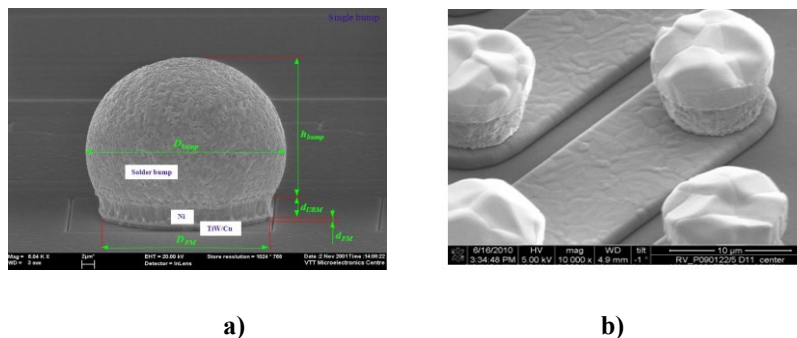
Exemples de billes [FC](#) de différentes variantes : a) bille de soudure de diamètre 20 µm [52], b) CuSn billes d'un diamètre de 10 µm [53].
